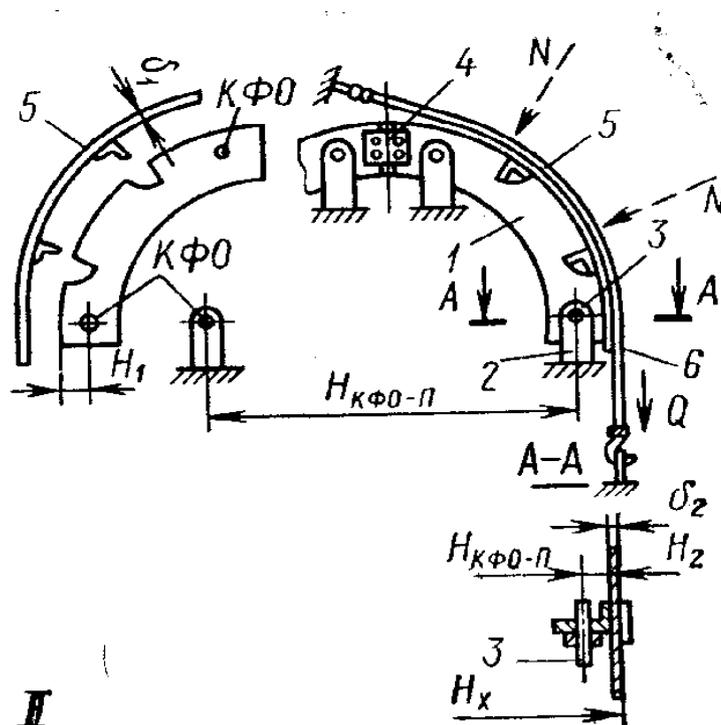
Базирование по КФО при установке элементов каркаса в сборочное положение: 1- шпангоут; 2- кронштейн сборочного приспособления; 3 – фиксатор; 4 – стык шпангоутов; 5 – прижим; 6 – натяжная лента; NN – направление усилий прижима.
